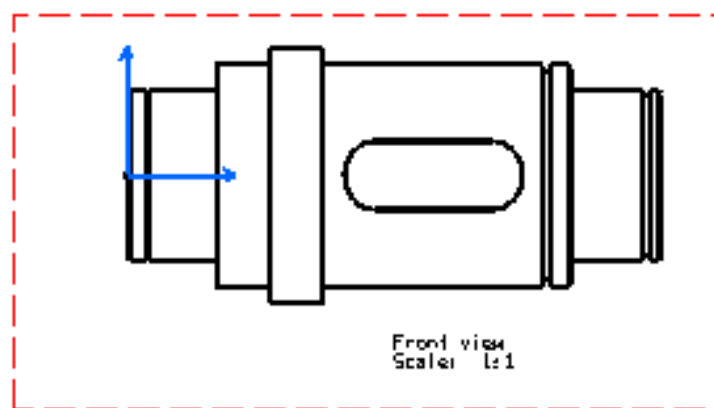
Přepnutí do pracovního prostředí ( Edit; Working Views )
